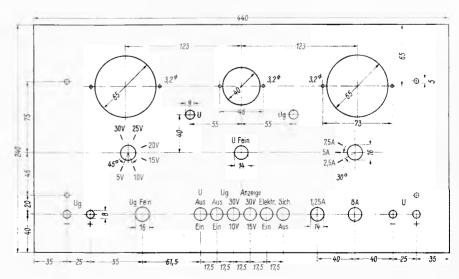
Abmessungen und Bohrungen der zweiten Frontplatte
